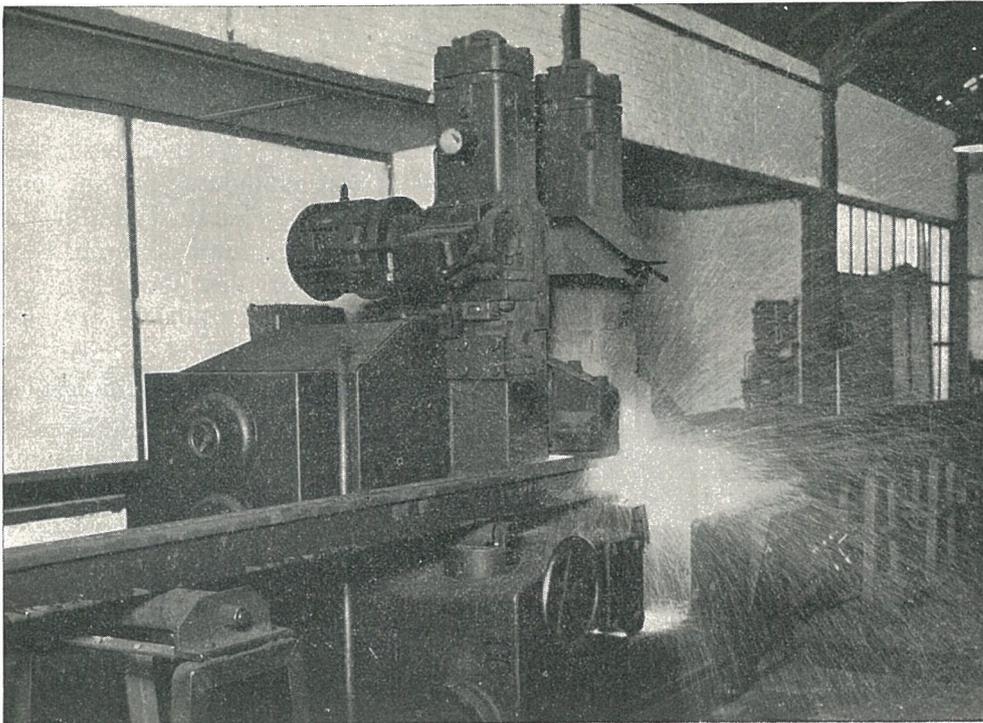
(1). — Machine électrique automatique à souder les rails bout à bout, en action.
